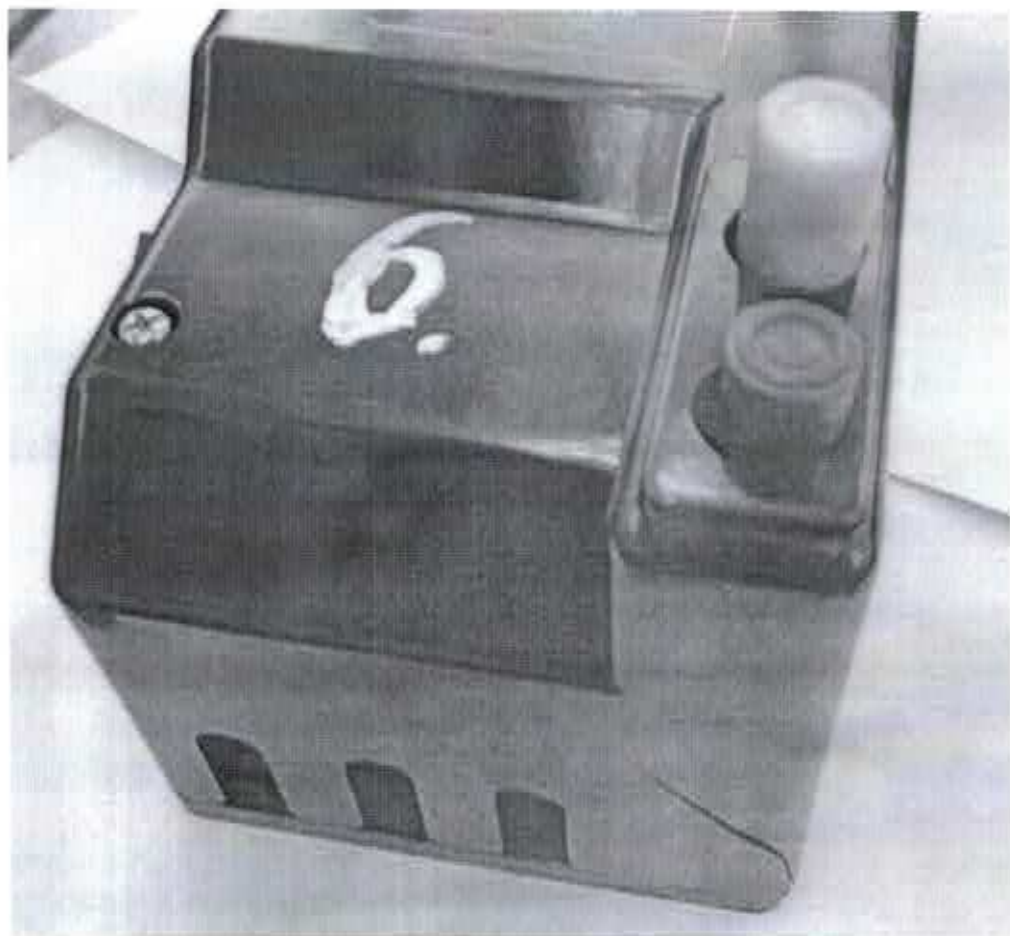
Образец № 6 после ПКС, трещина крышки
